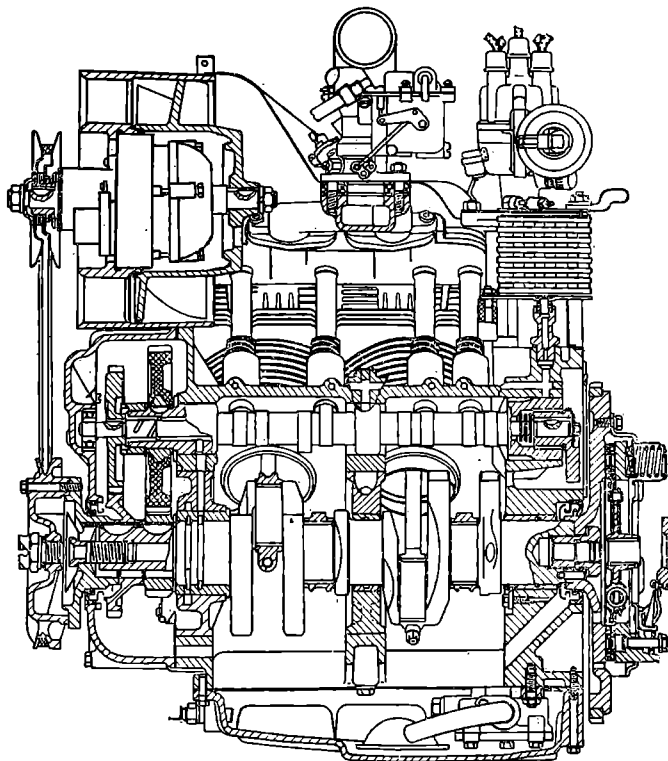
Продольный разрез двигателя МеМЗ-968.
